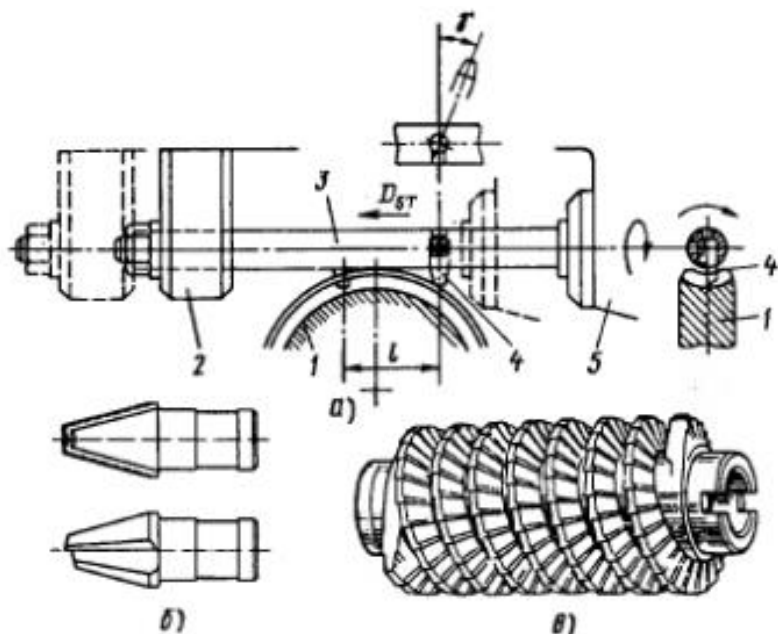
Схеми фрезерування зубів черв'ячного колеса фрезою-летучкою (а), черв'ячним швером (в); різці чорновий та чистовий (б) для установки на оправці
